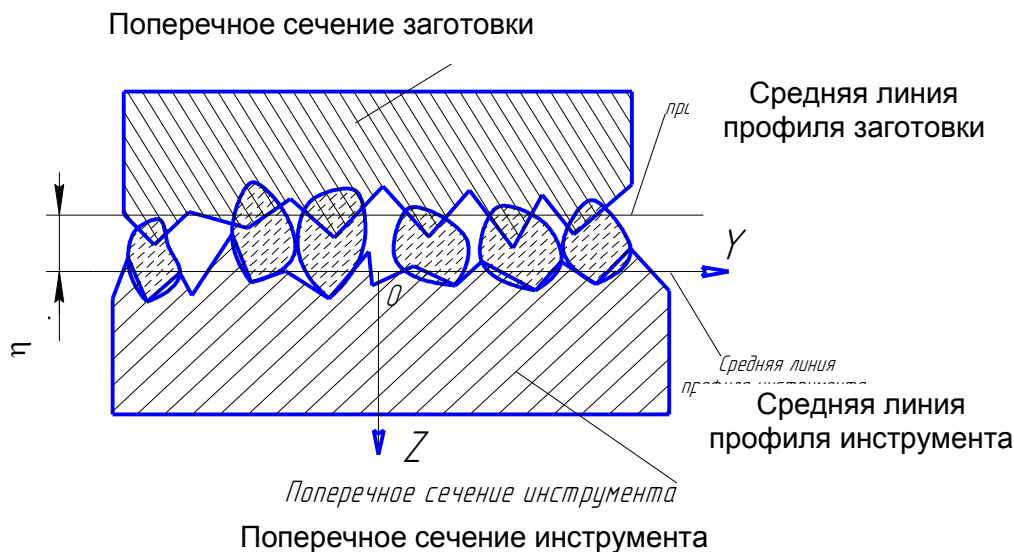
Схема контакта поверхности заготовки с поверхностью доводочного инструмента
